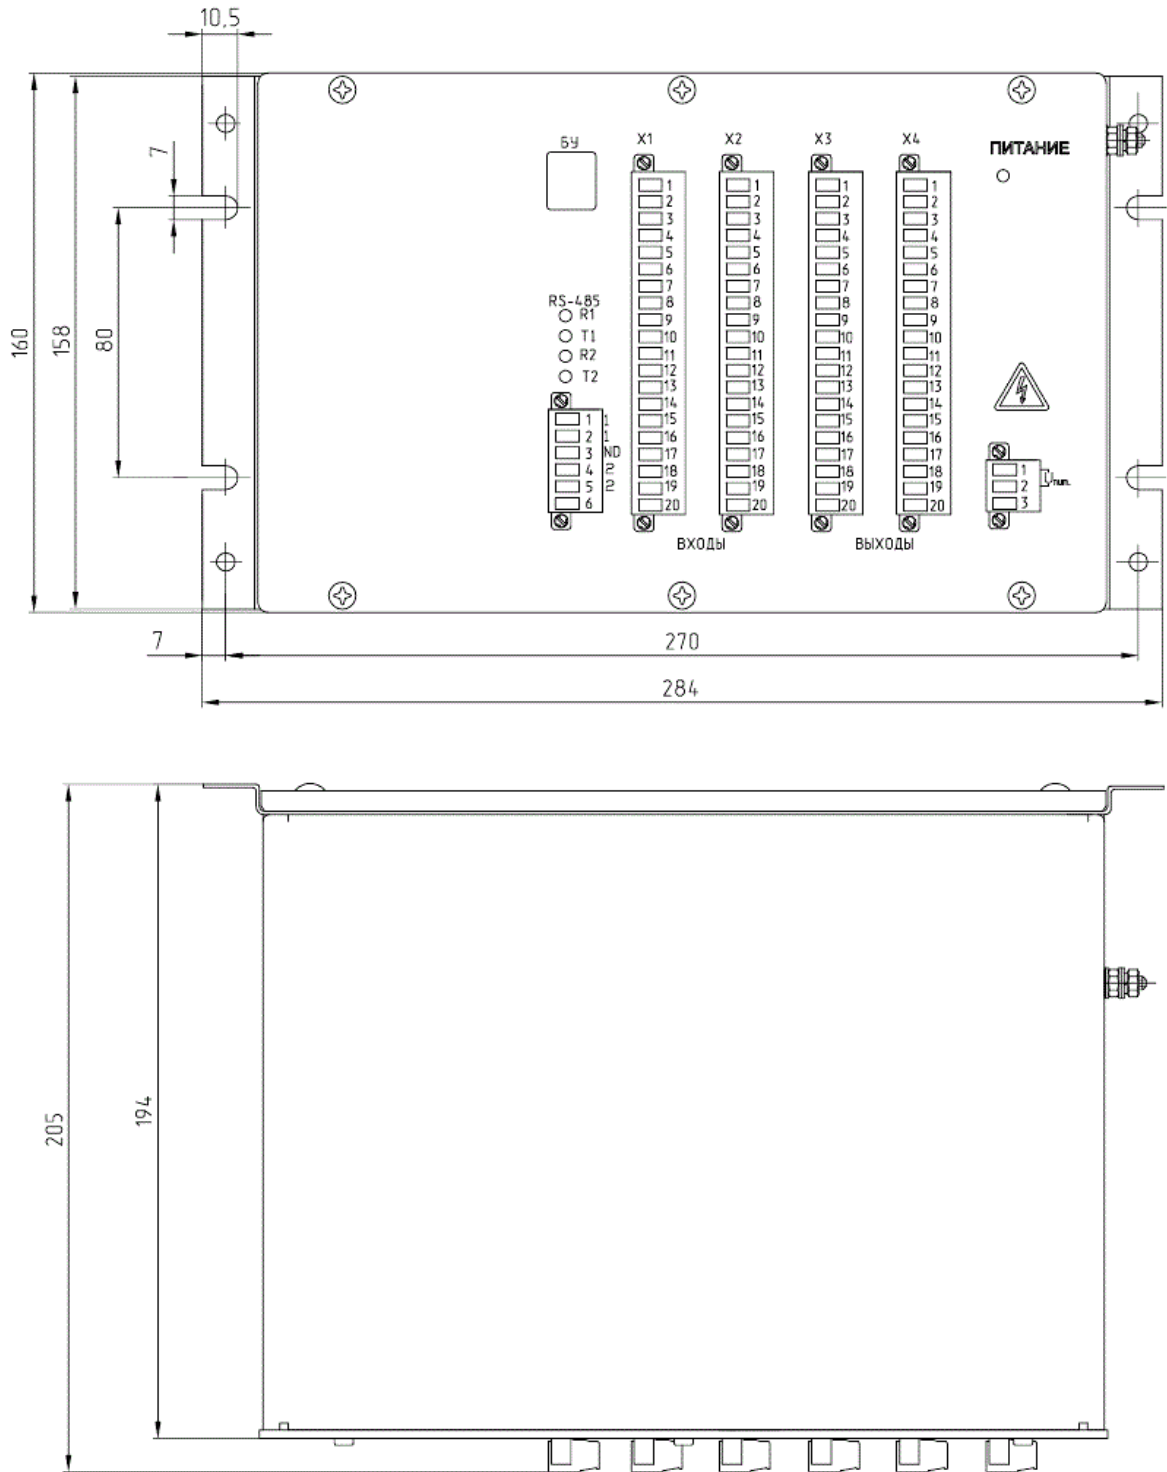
Габаритные и установочные размеры блока контроллера
